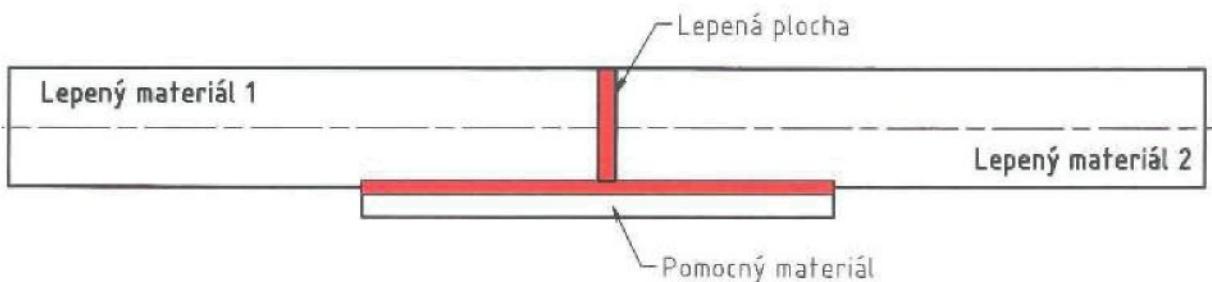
Vyobrazení konstrukce lepeného spoje tupého
